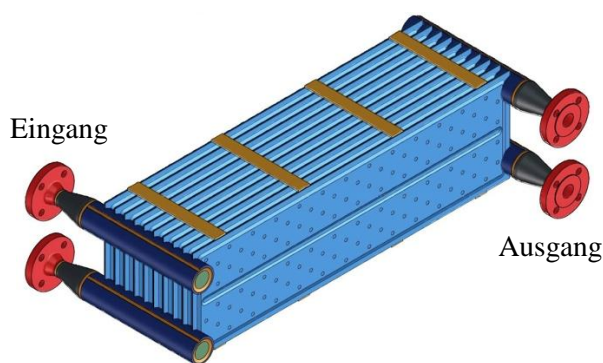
CAD-Zeichnung des Thermoblechregisters
